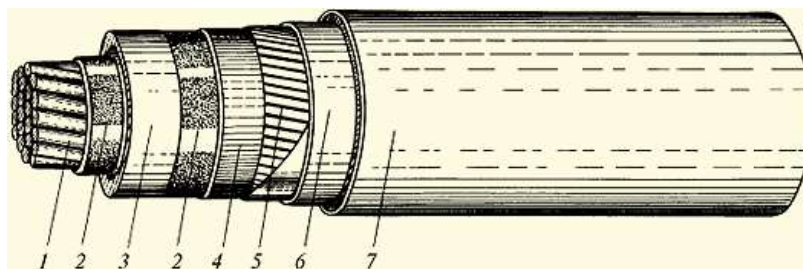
Конструкция кабеля на 10 кВ: 1 - токопроводящая жила; 2 - электропроводящие экструдированные экраны; 3 - изоляция; 4 - электропроводящие влагонабухающие ленты; 5 - экран из медных проволок; 6 - разделительная обмотка лентой; 7 - оболочка
